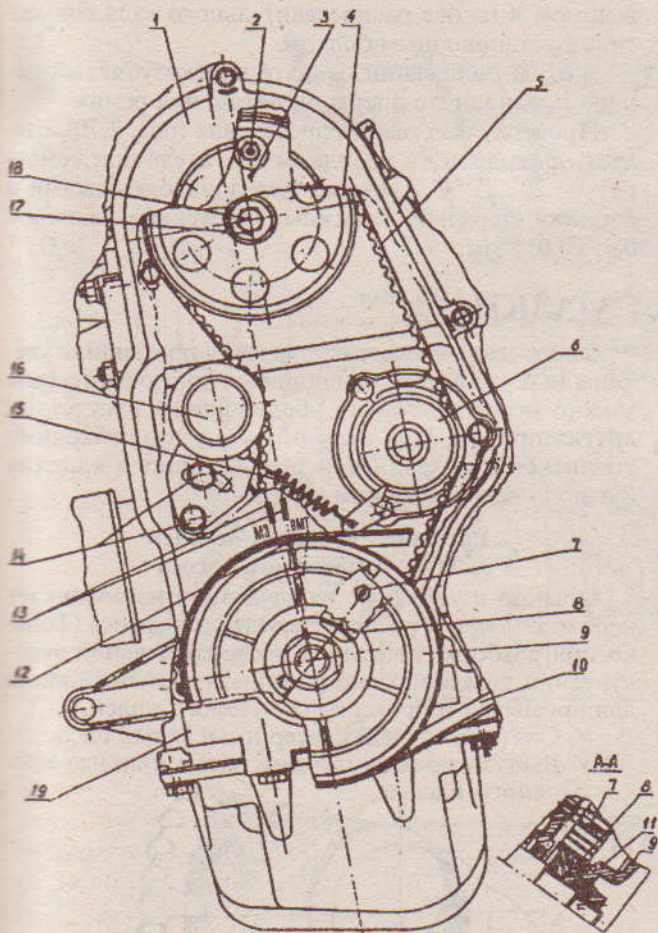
Привод распределительного вала: 1 - наружный кожух плосkozубчатого ремня; 2 - стрелка установки ведомого шкива распределительного вала; 3 - метка на шкиве распределительного вала; 4 - ведомый шкив распределительного вала; 5 - плосkozубчатый ремень; 6 - шкив водяного насоса; 7 - стрелка установки ведущего шкива привода распределительного вала в ВМТ; 8 - ведущий шкив привода распределительного вала; 9 - шкив привода генератора; 10 - ремень привода генератора; 11 - метка ВМТ (сверленное гнездо диаметром 4 мм) на ступице шкива привода генератора; 12 - метка ВМТ на шкиве привода генератора (Прорез на наружной стороне шкива); 13 - метки ВМТ и МЗ на верхнем кожухе зубчатого ремня; 14 - болты кронштейна натяжного ролика; 15 - пружина натяжного ролика; 16 - натяжной ролик; 17 - отгибная шайба; 18 - болт крепления шкива; 19 - упор верхнего кожуха
